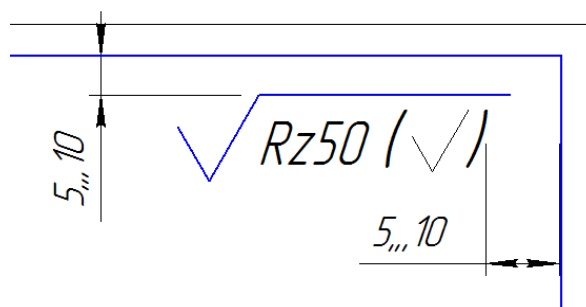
Обозначение неуказанной шероховатости поверхности
